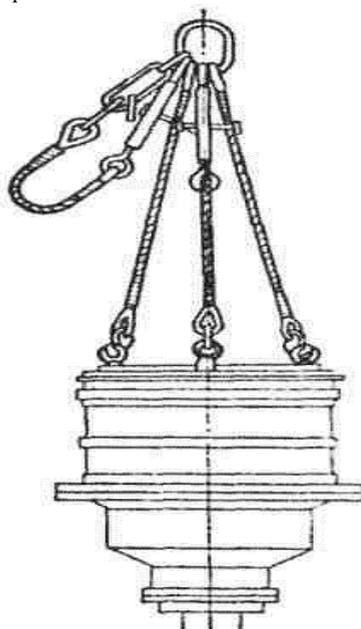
Зачаливание коробки передач приспособлением ЧПУ-С6Б с использованием рымболтов РБ-1С6 и РБ-2С6
